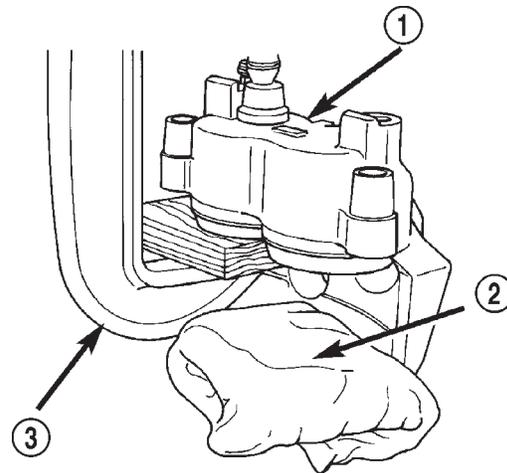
Einen Kolben mit Schraubzwinge fixieren
